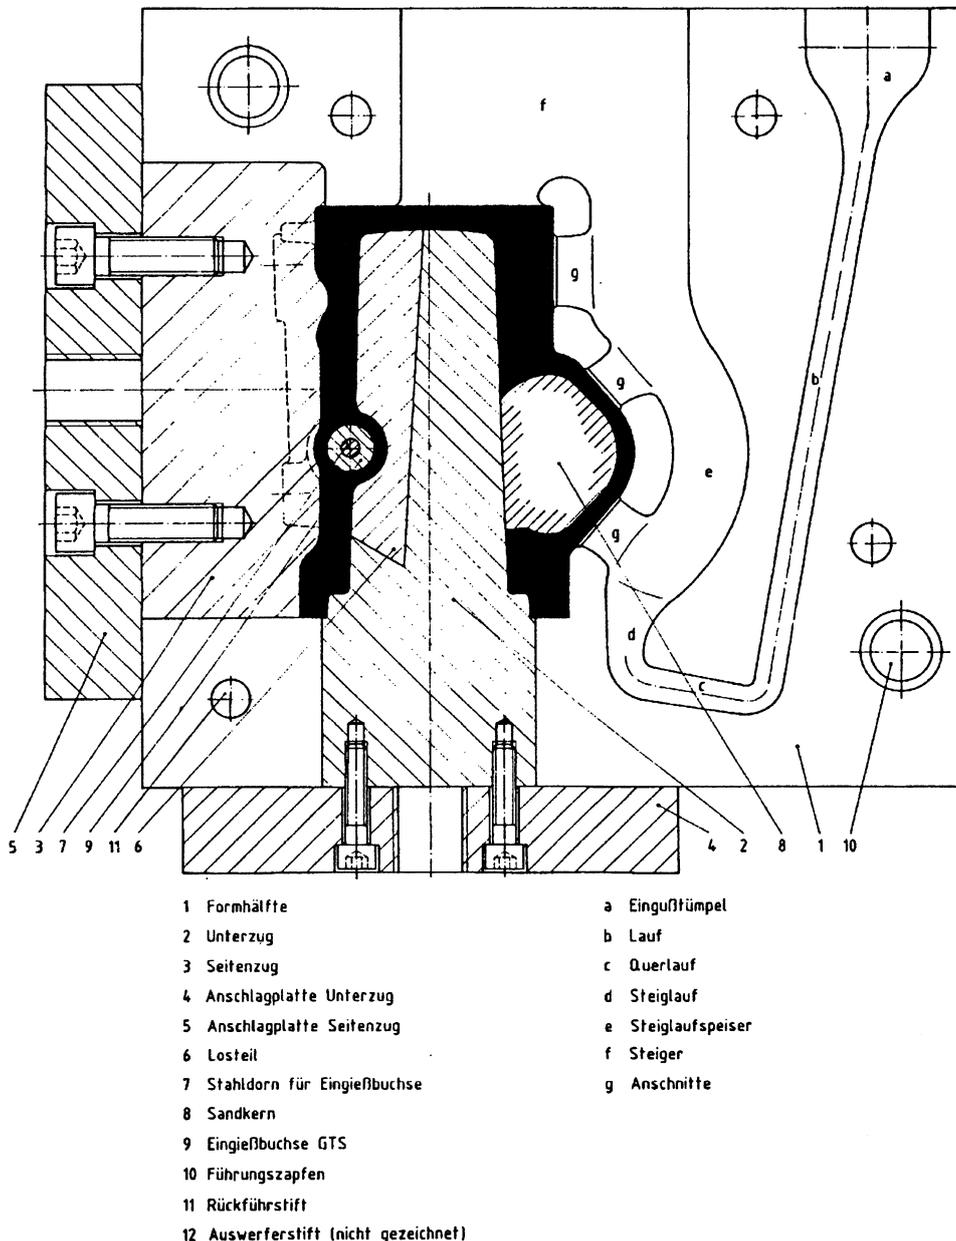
Beispiel einer Kokillenzzeichnung: PKW-Lenkgehäuse
